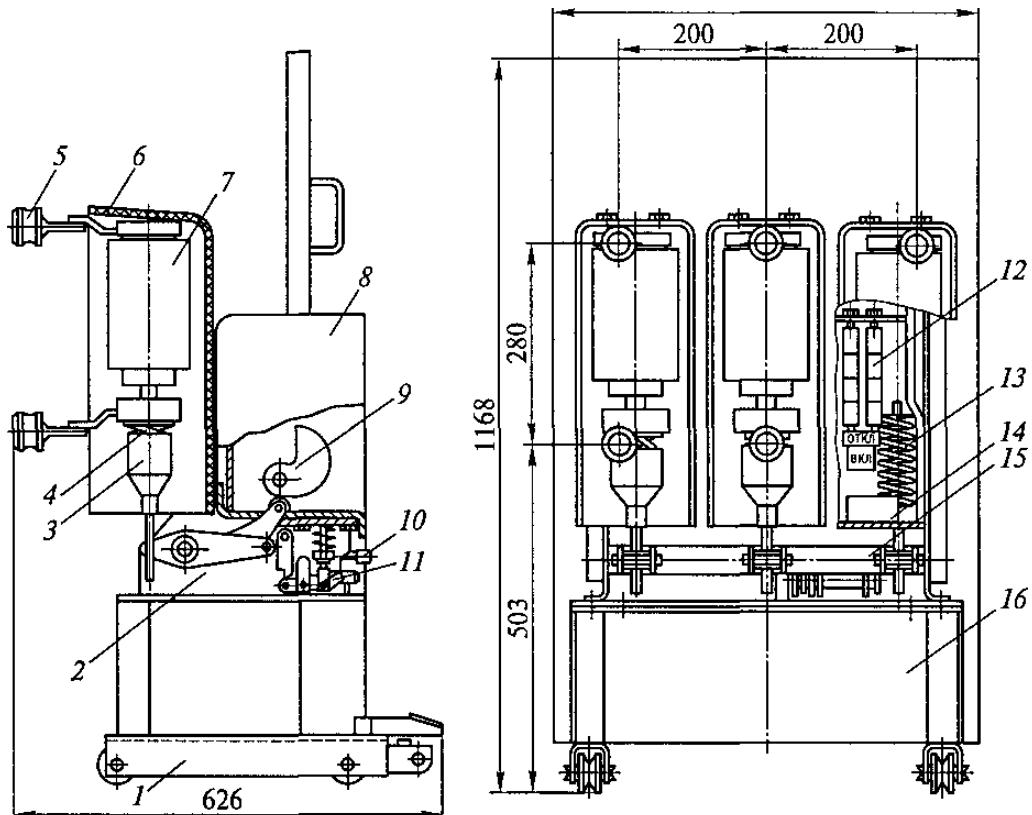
Выключатель вакуумный ВБП-С-10-31,5/1600 УЗ:
